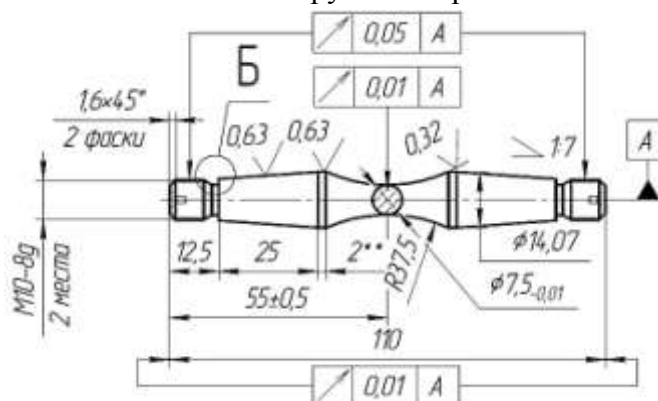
Гладкий цилиндрический образец с рабочей частью переменного сечения для испытаний по схеме нагружения «чистый изгиб с вращением»
